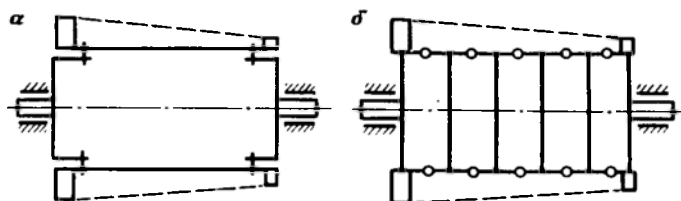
Конструктивные схемы барабанного (а) и барабанно-дискового ротора (б) осевых компрессоров
